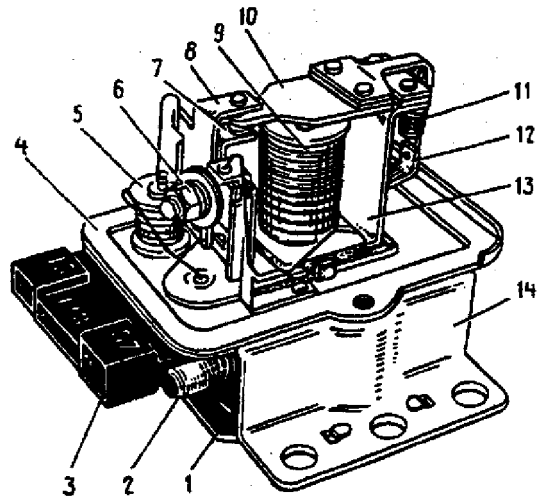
Regulador de tensão: 1 - placa protetora; 2 - resistor complementar; 3 - flange inferior com alojamentos dos terminais "15" e "67"; 4 - junta da tampa; 5 - bobina de reação; 6 - porca de fixação dos montantes; 7 - montante do platinado superior; 8 - montante do platinado inferior; 9 - bobina do regulador; 10 - induzido; 11 - mola do induzido; 12 - suporte da mola; 13 - cabeçote; 14 - base.
